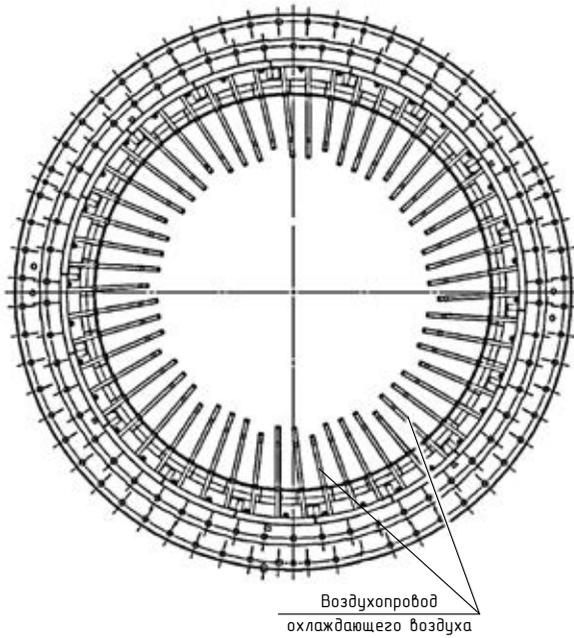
Корпус 1-й ступени ТНД (силовой)
